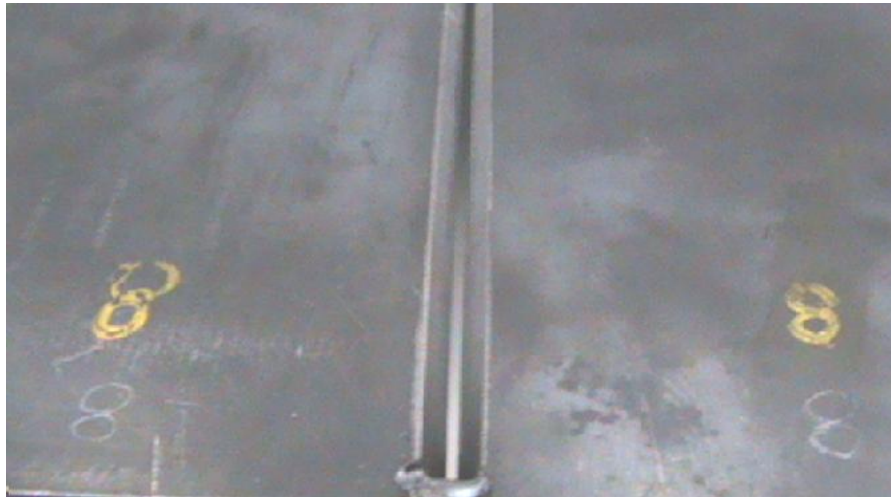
Fotografia da junta de topo antes da soldagem
